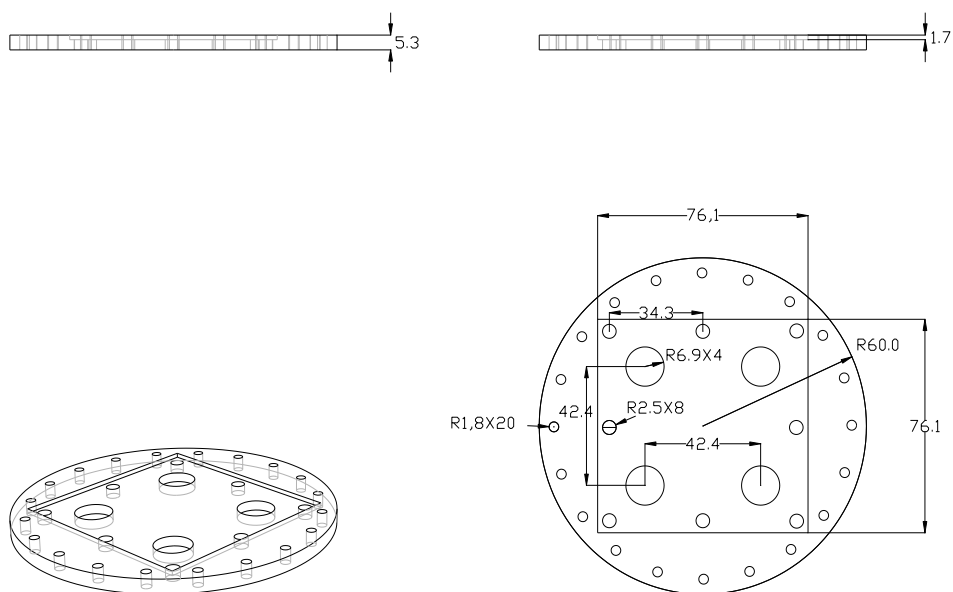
Planimetría placa superior SHIELD⁵⁵
